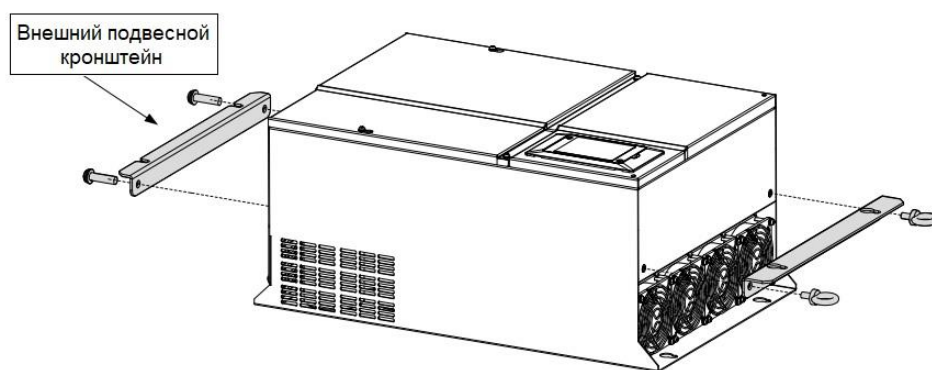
Монтаж в сквозное отверстие устройства INVERTER (корпус из листового металла)
